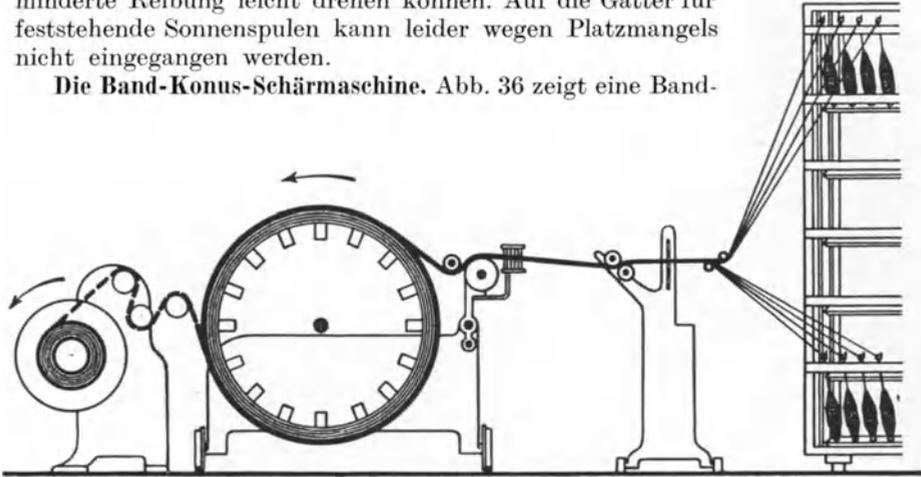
Lauf der Kette durch eine Konus-Kettenschärmaschine.
